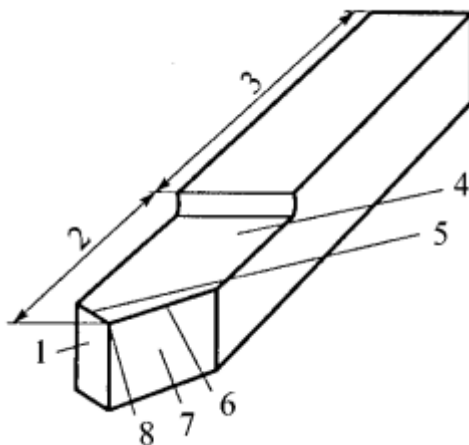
Элементы токарного прямого проходного резца: 1 – вспомогательная задняя поверхность; 2 – головка резца; 3 – тело резца; 4 – передняя поверхность; 5, 6 – вспомогательная и главная режущие кромки соответственно; 7 – главная задняя поверхность; 8 – вершина резца
